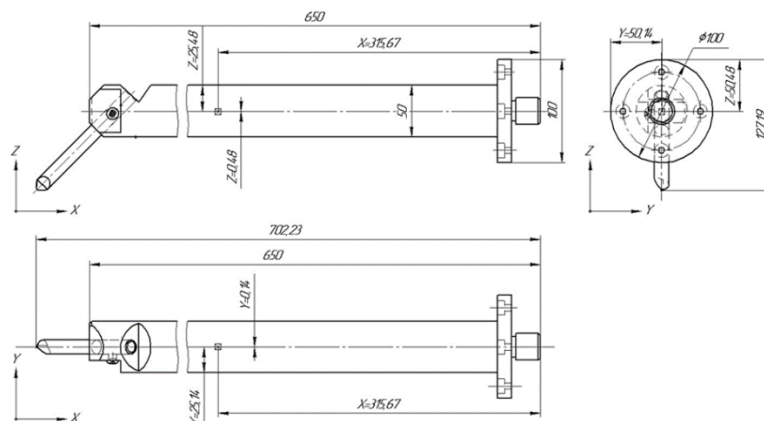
Креслення проекцій борштанги без противаги з визначеними відхиленнями координат центра ваги від вісі обертання
